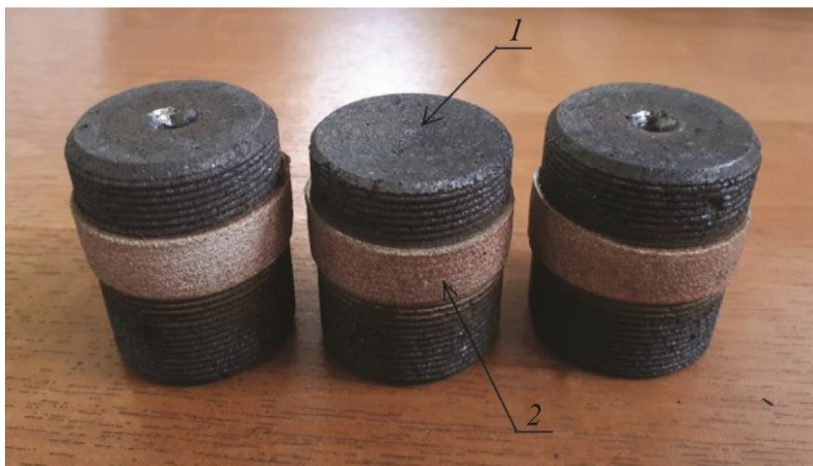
Образцы для определения прочности сцепления покрытий: 1 – графитированный материал; 2 – плазменно-порошковое покрытие
